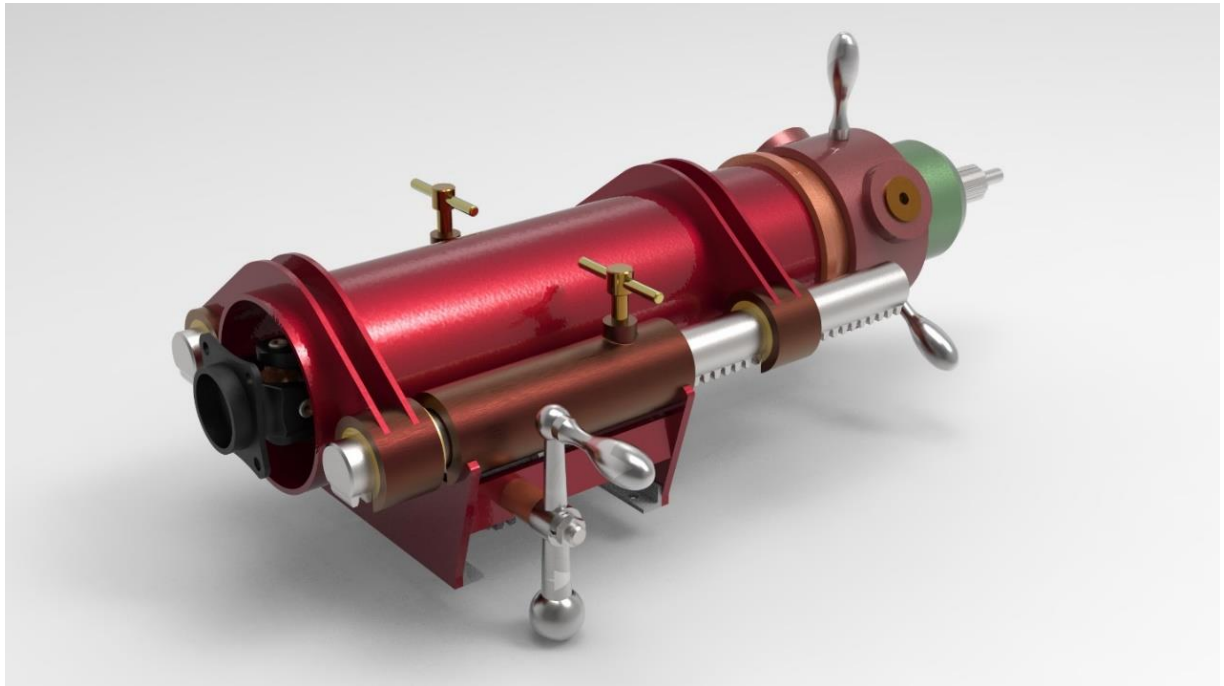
Пристрій для з'єднання вала обкатувально-гальмівного стенда із валом двигуна: 1 – вал карданний шліцьовий; 2 – вилка; 3 – корпус; 4 – хрестовина; 5 – вал-рейка; 6 – вал шліцьовий; 7 – втулка; 8 – втулка рейки; 9, 10 – втулка розпірна; 11 – гвинт; 12 – кожух (не показано); 13 – обойма; 14 – обойма корпусу; 15 – основа; 16 – пружина; 17 – ручка; 18 – ручка маховика; 19 – стакан; 20 – стакан пружини; 21 – ступиця шліцьова; 22 – труба; 23 – труба карданна; 24 – шестерня; 25 – шпилька; 26 – болт; 27, 28 – гайка; 29 – кільце; 30 – манжета; 31, 32 – підшипник; 33 – прокладка регулювальна; 34 – шайба пружинна; 35 – шпонка.
